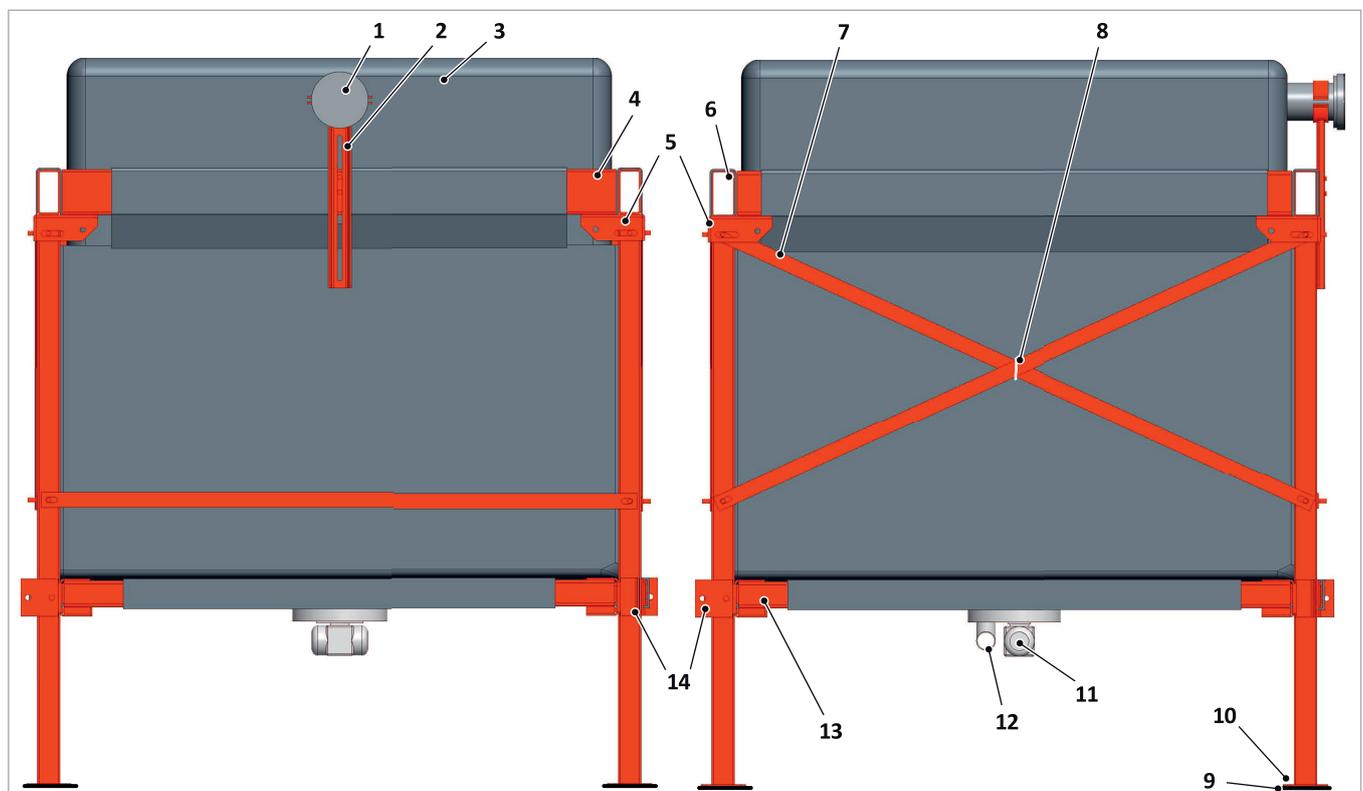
Bauteile des SolvisLinotanks (ab Baugröße 2,54 m Ausführung mit zwei nebeneinanderliegenden Füllrohren, Pos. 1)
